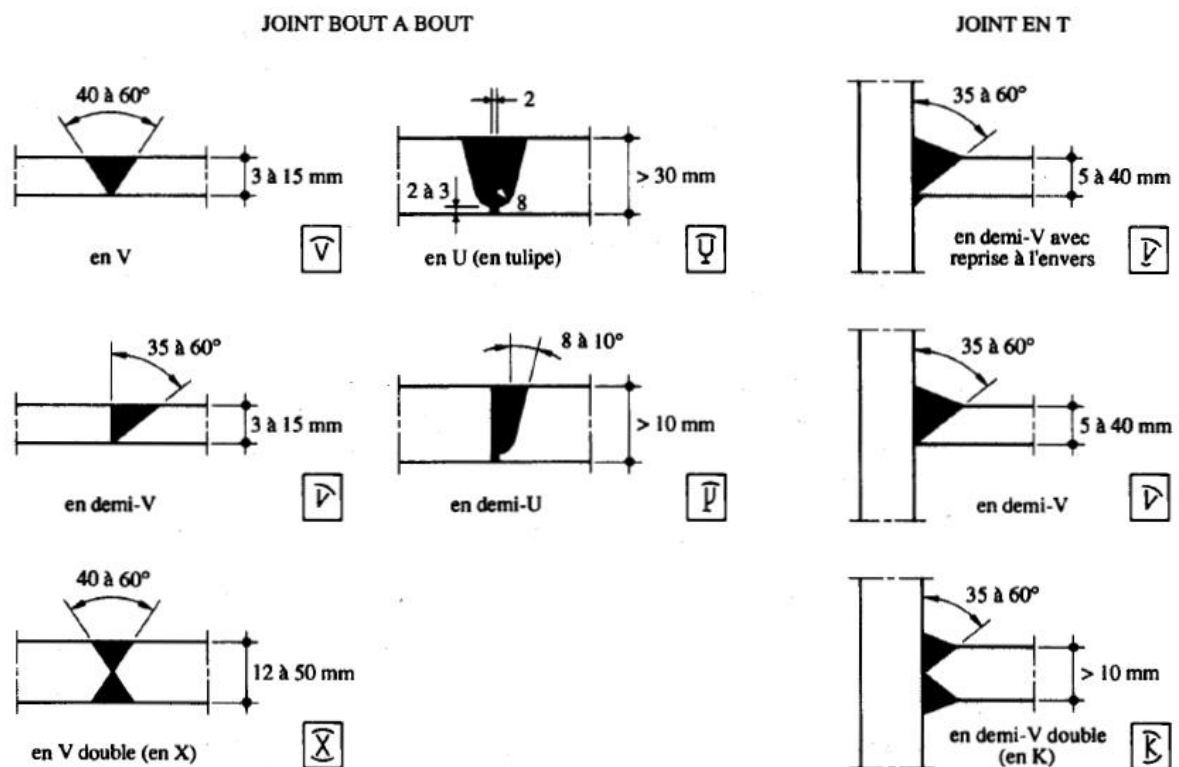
Exemples de soudures complètement pénétrées.
